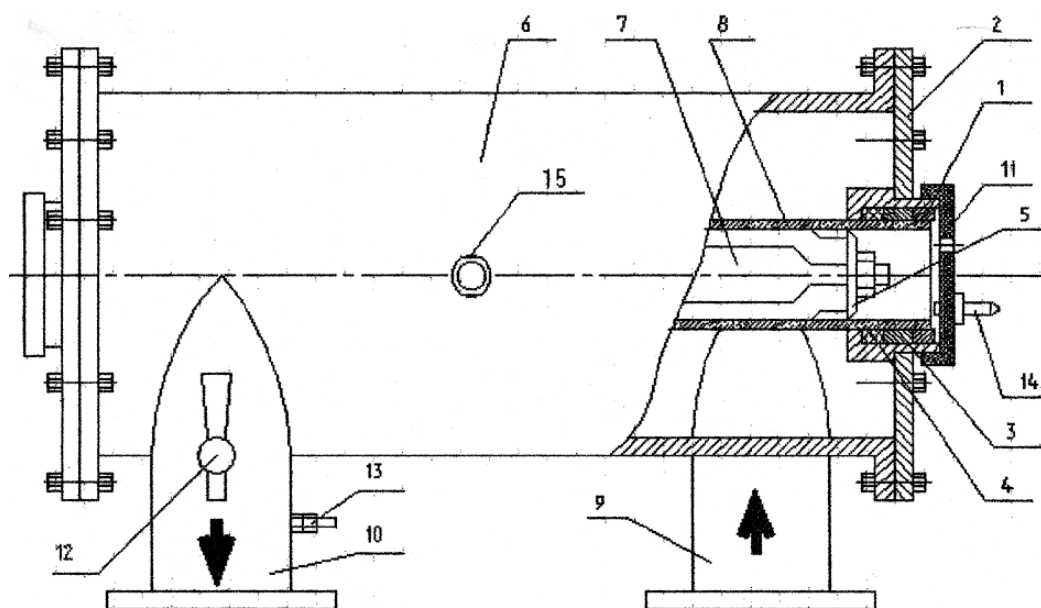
Камера обеззараживания УОВ-50ДМ: 1 – гайка нажимная; 2 – крышка; 3 – кольцо нажимное; 4 – манжета; 5 – держатель; 6 – корпус; 7 – лампа; 8 – кварцевая труба; 9 – патрубок входной; 10 – патрубок выходной; 11 – крышка резиновая; 12 – кран пробно-спускной; 13 – узел заземления; 14 – ниппель; 15 - глазок
